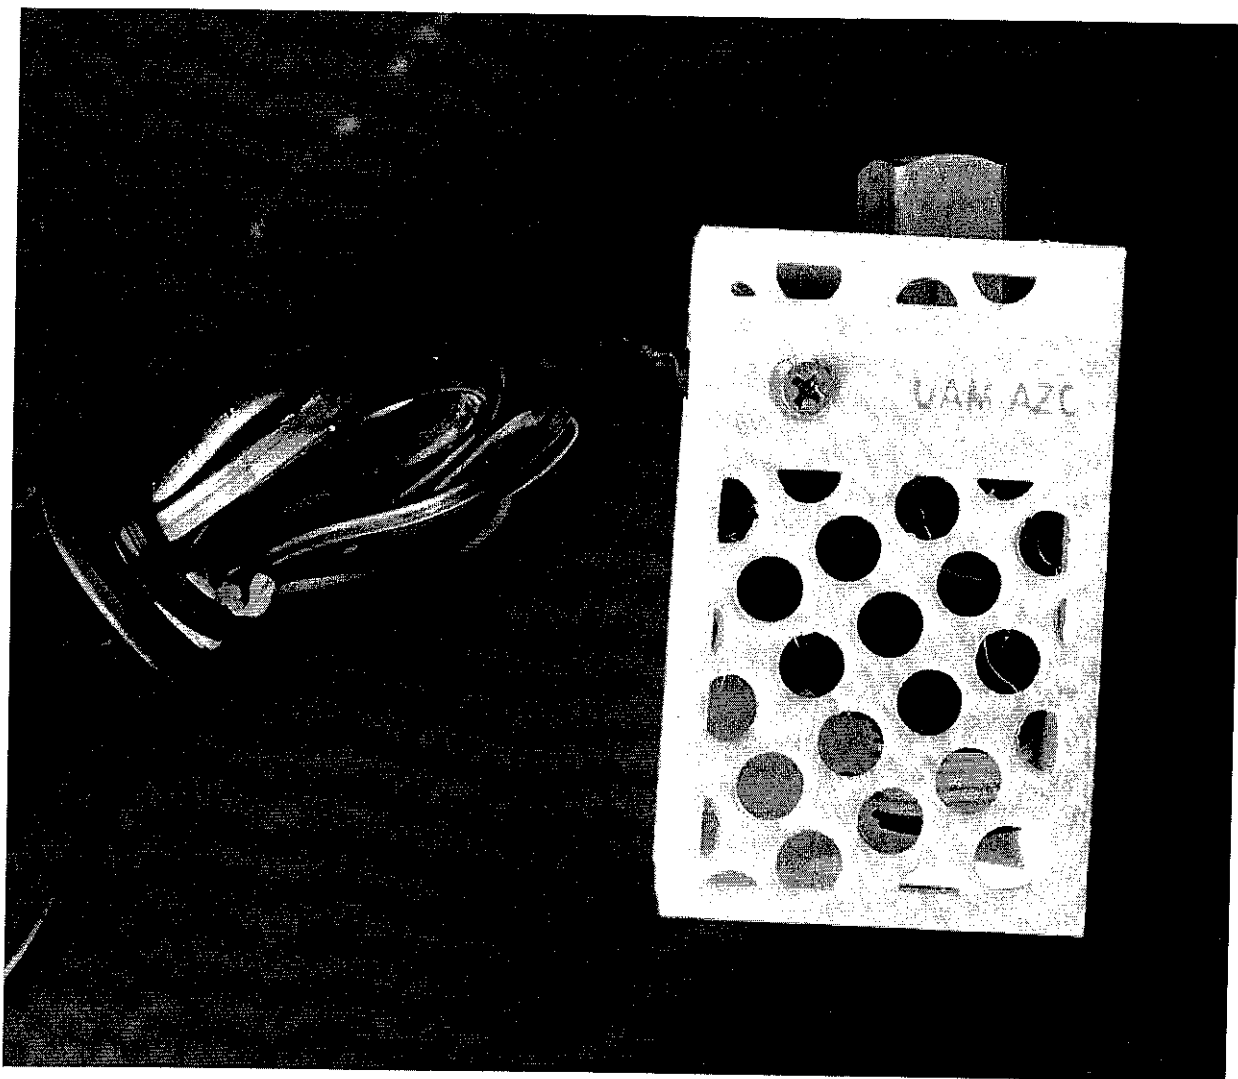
Ensamble carcaza, chasis y sensor de flujo (vista superior)
